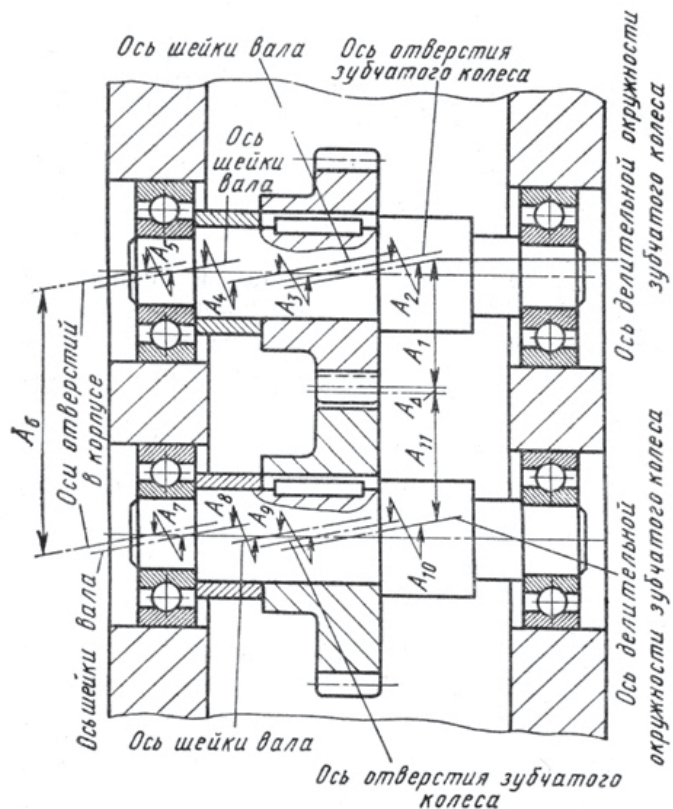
Схема размерной цепи A_{Δ} , определяющей расстояние между образующими делительных цилиндров двух зубчатых колес
